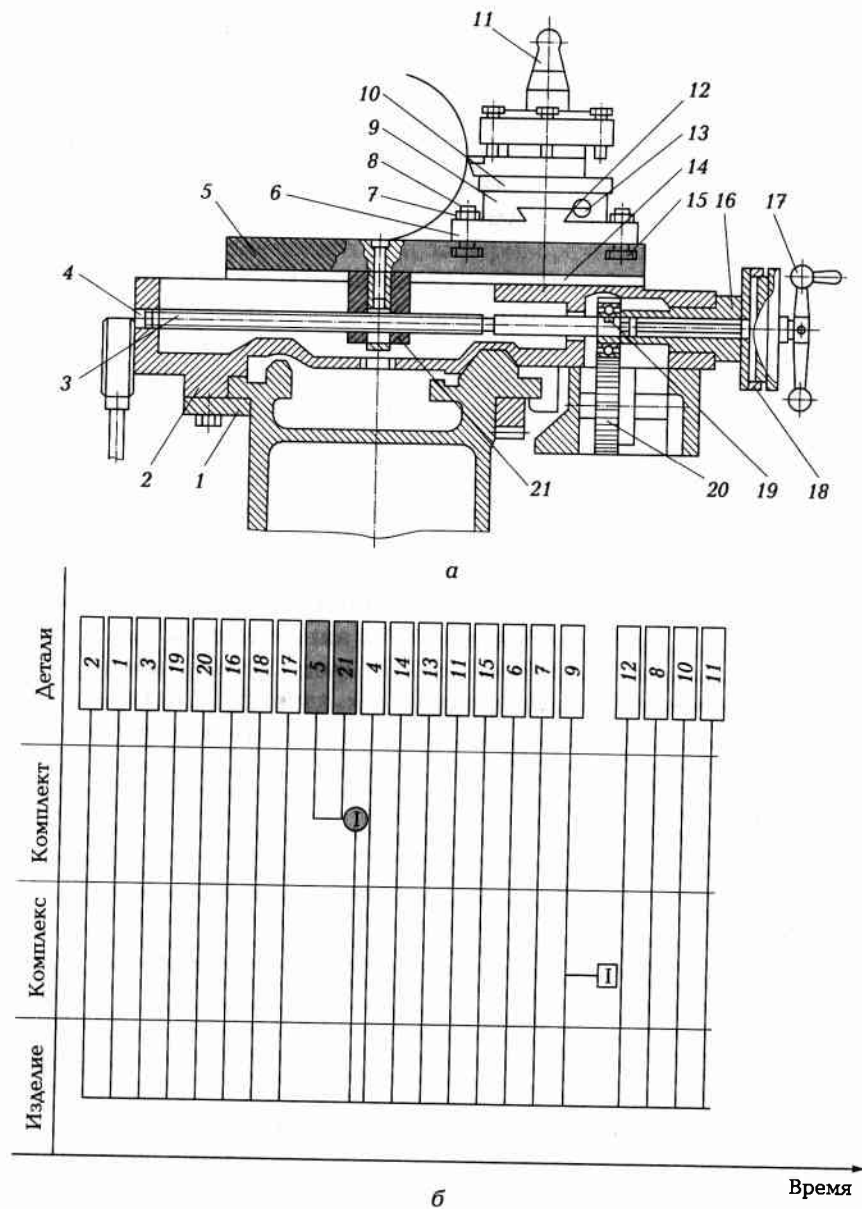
Суппортная группа токарно-винторезного станка (а) и схема ее сборки (б)
